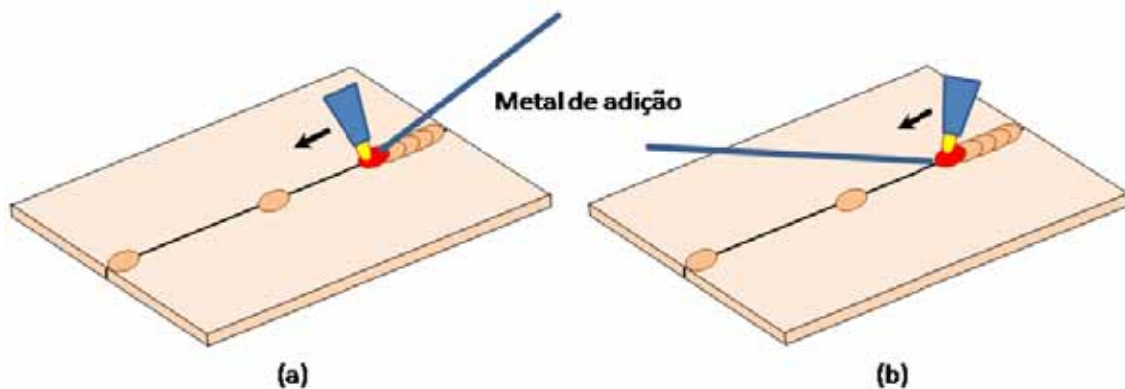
Técnicas de execução: (a) Soldagem para trás e (b) soldagem para frente.
